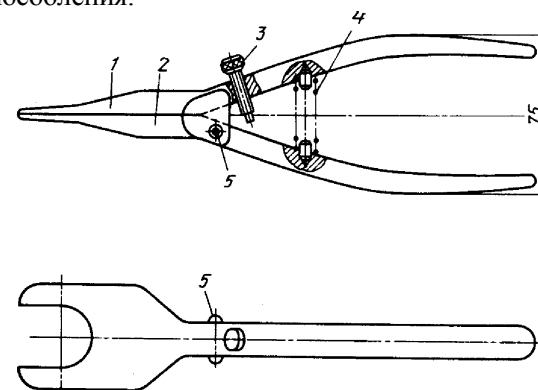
Приспособление для снятия резиновых шлангов
